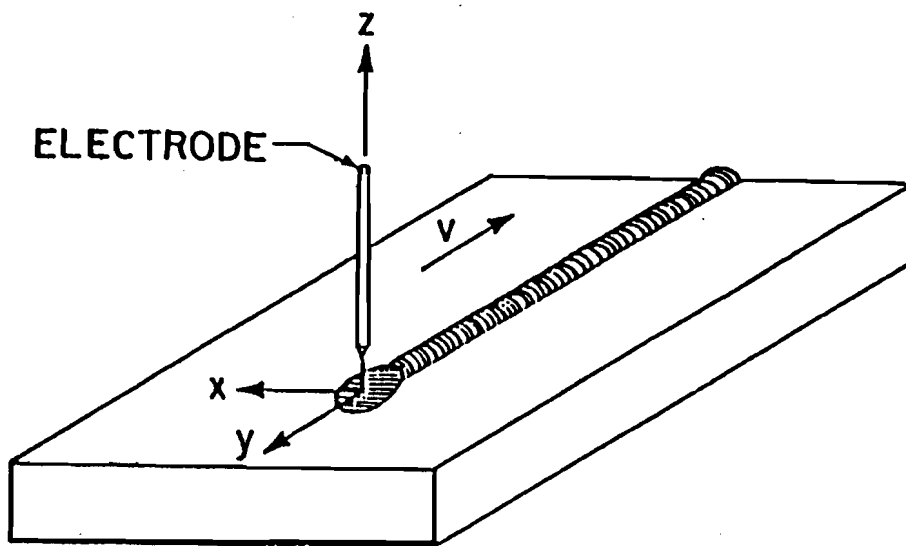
Ilustración de una soldadura a lope GMA.
